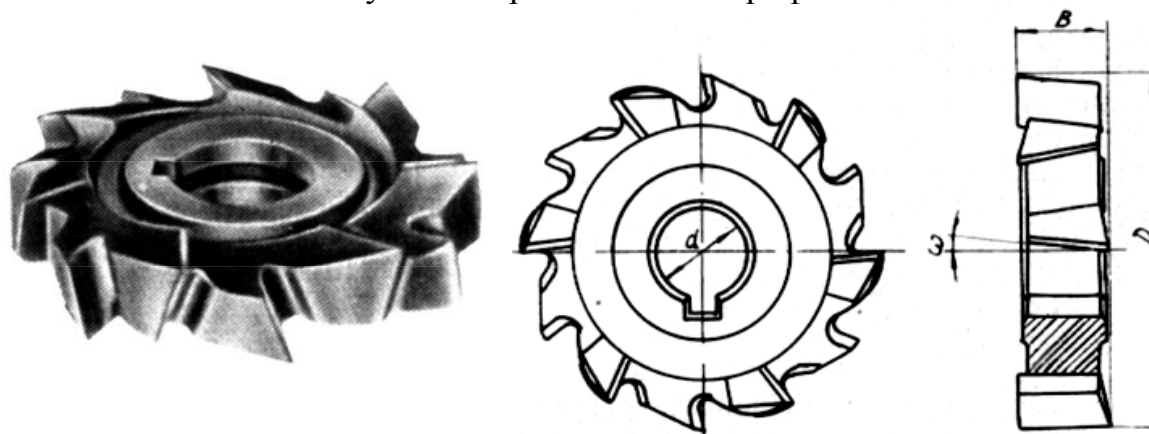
Современная конструкция цельной дисковой фрезы с трехсторонней схемой резания
